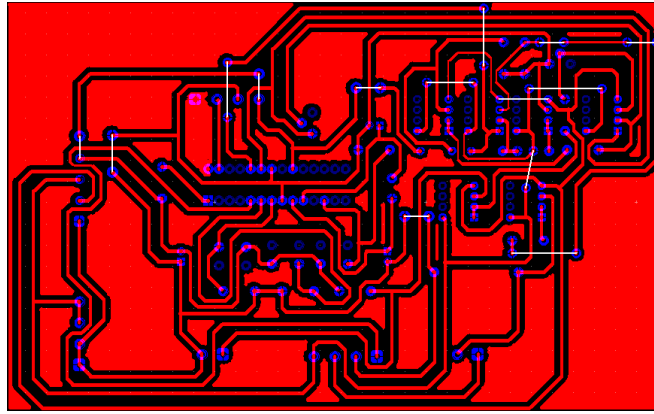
Layout cara BOTTOM donde se sitúan las pistas.
